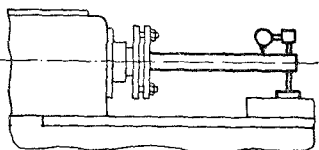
Проверка центров делительной головки и задней бабки у шлицефрезерного станка.
